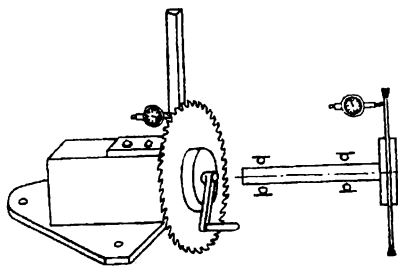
Внешний вид и схема устройства прибора ПНТ для оценки торцового биения
